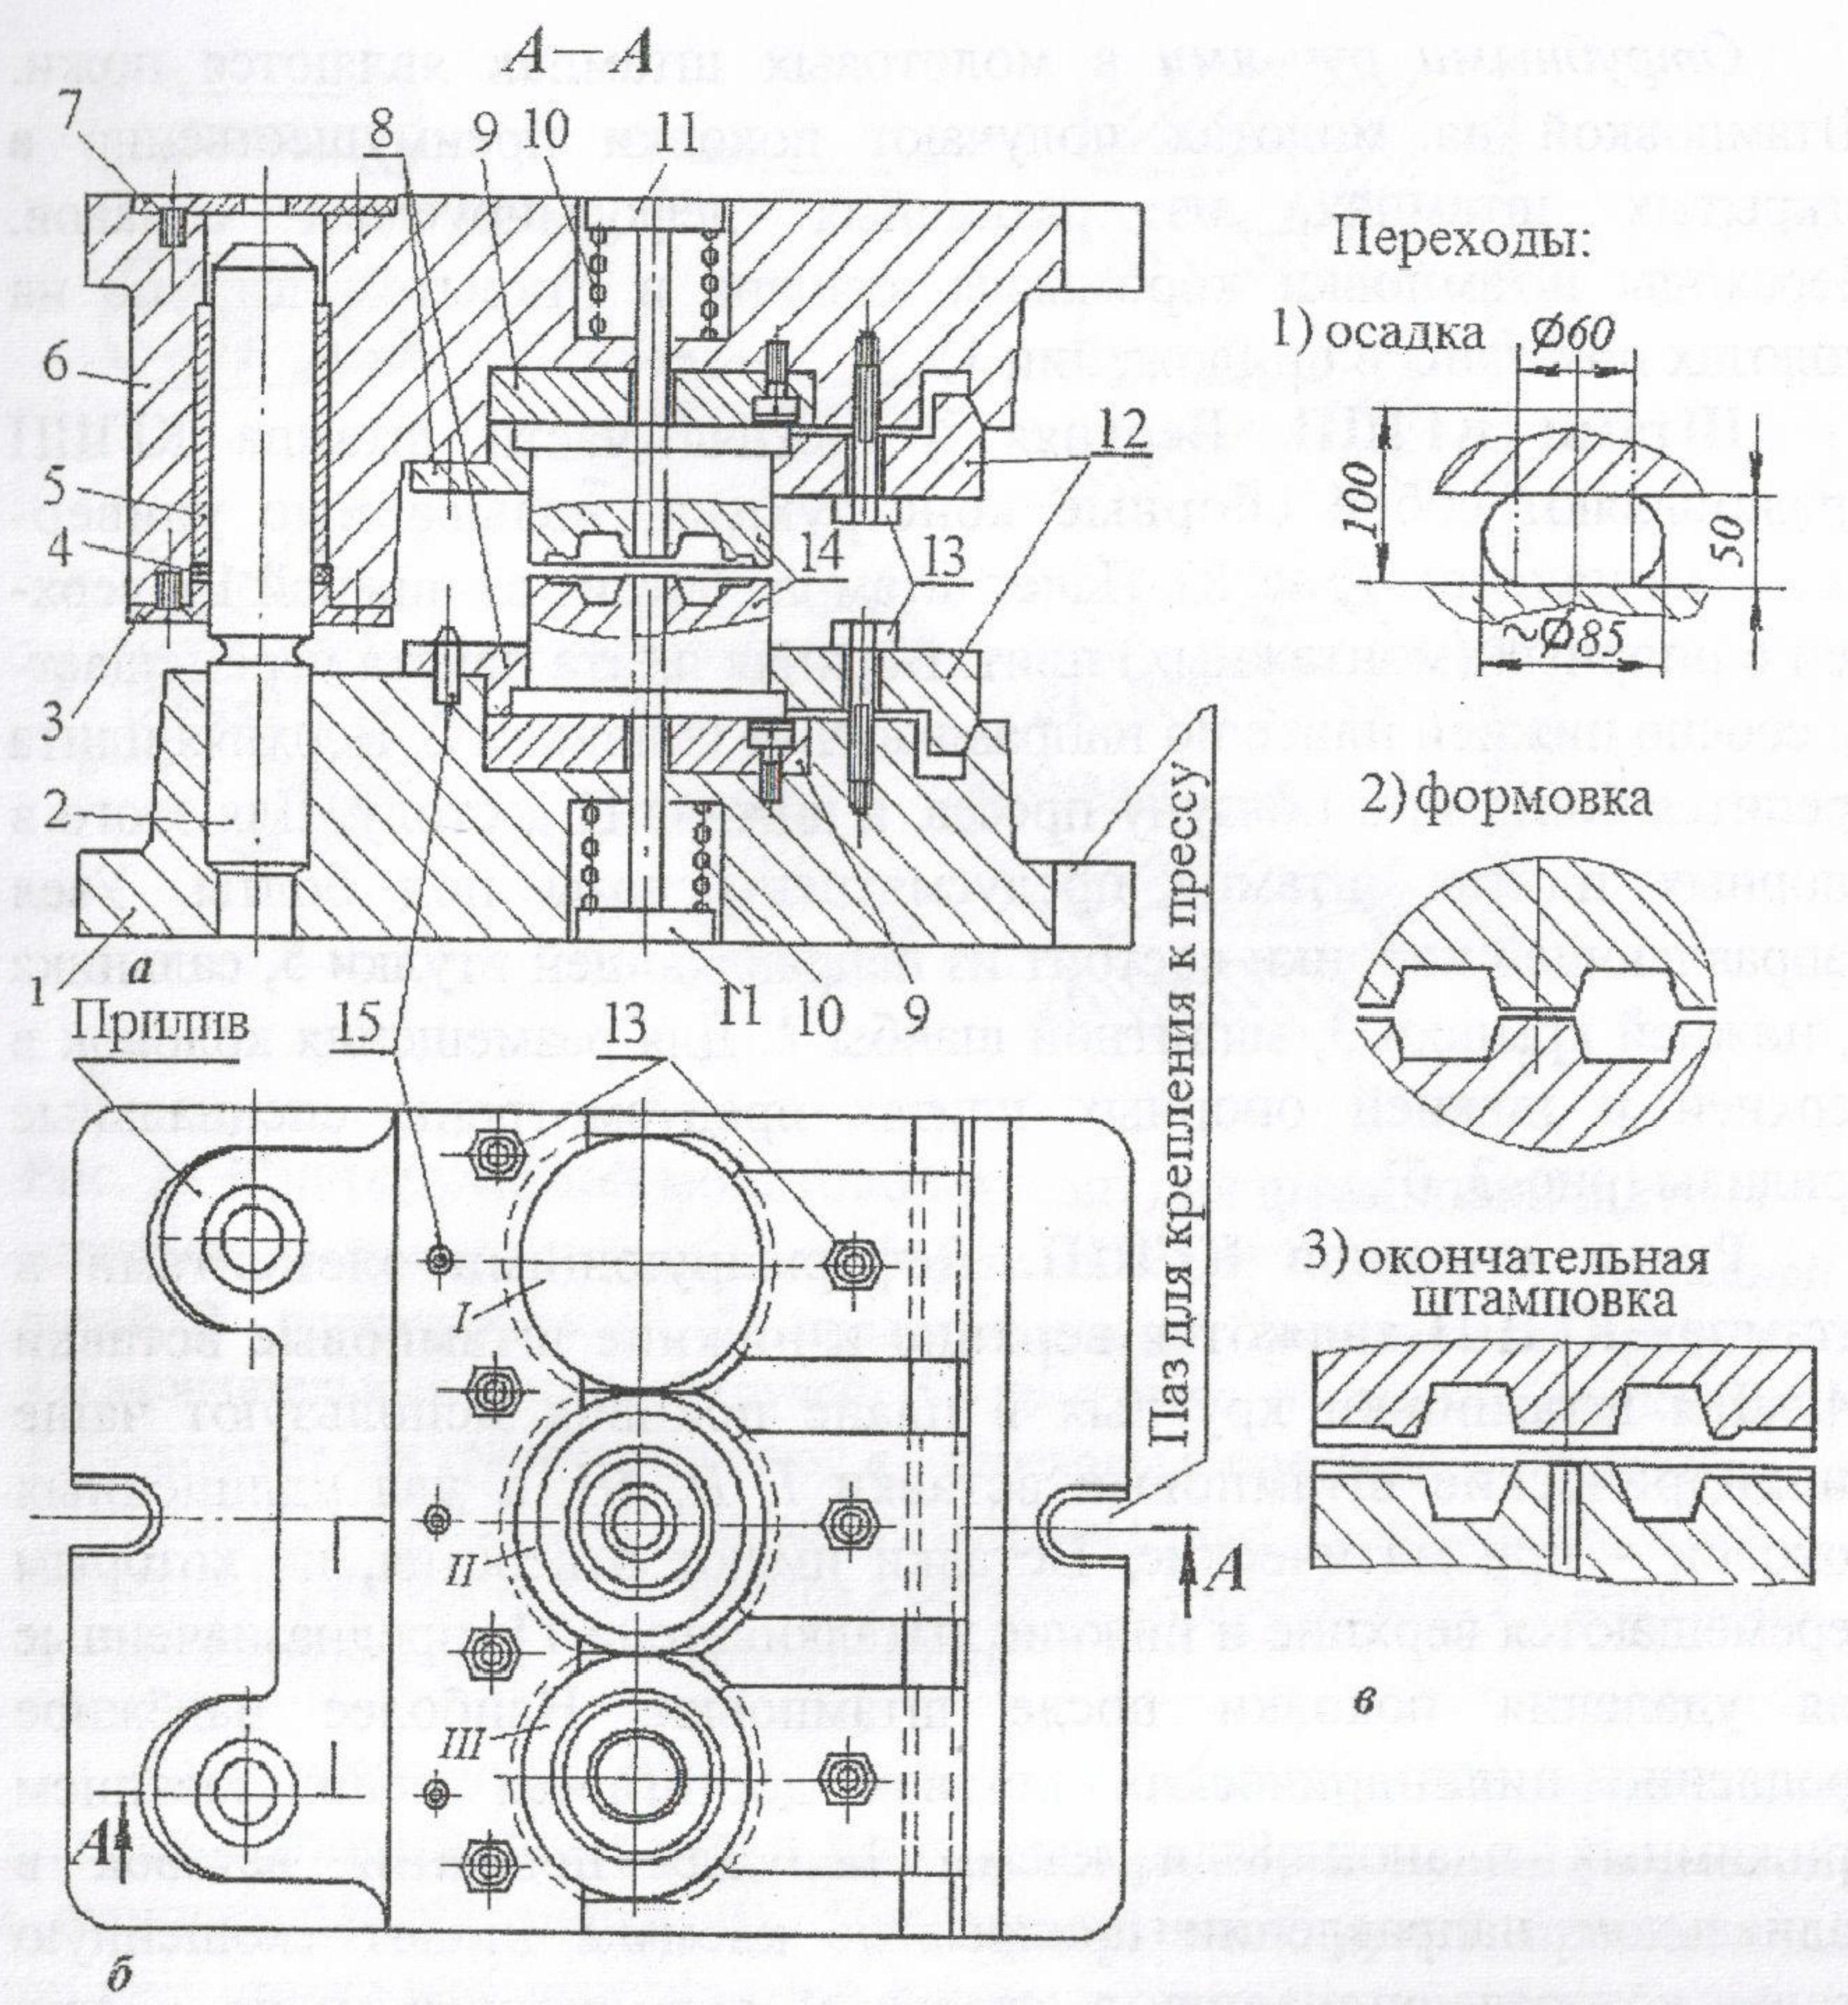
Штамп КГШП для изготовления поковки детали типа «втулка»: а – разрез штампа; б – вид сверху (при снятом верхнем штампе); в – переходы штамповки; 1 – нижняя опорная плита; 2 – колонка направляющая; 3 – крышка нижняя; 4 – сальник; 5 – втулка направляющая; 7 – шайба защитная; 8 – планка прижимная; 9 – плита подштамповая; 10 – пружина; 11 – выталкиватели; 12 – клеммы прижимные; 13 – болты; 14 – вставки; 15 – штыри центрирующие; I, II, III – вставки
